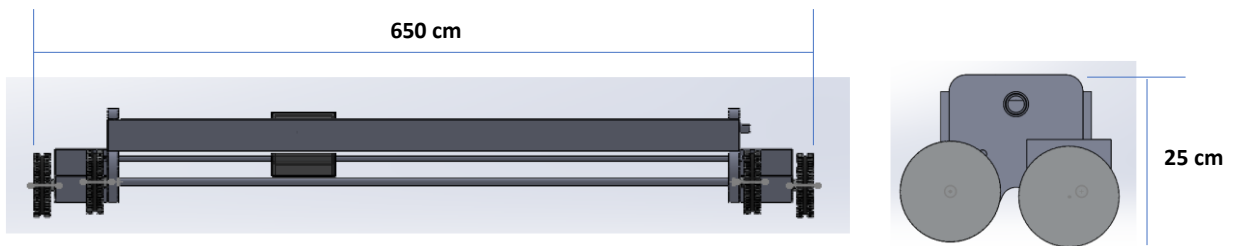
Sistema robotizado para inspección de tanques propuesto \_ INSPECRBOTRK
